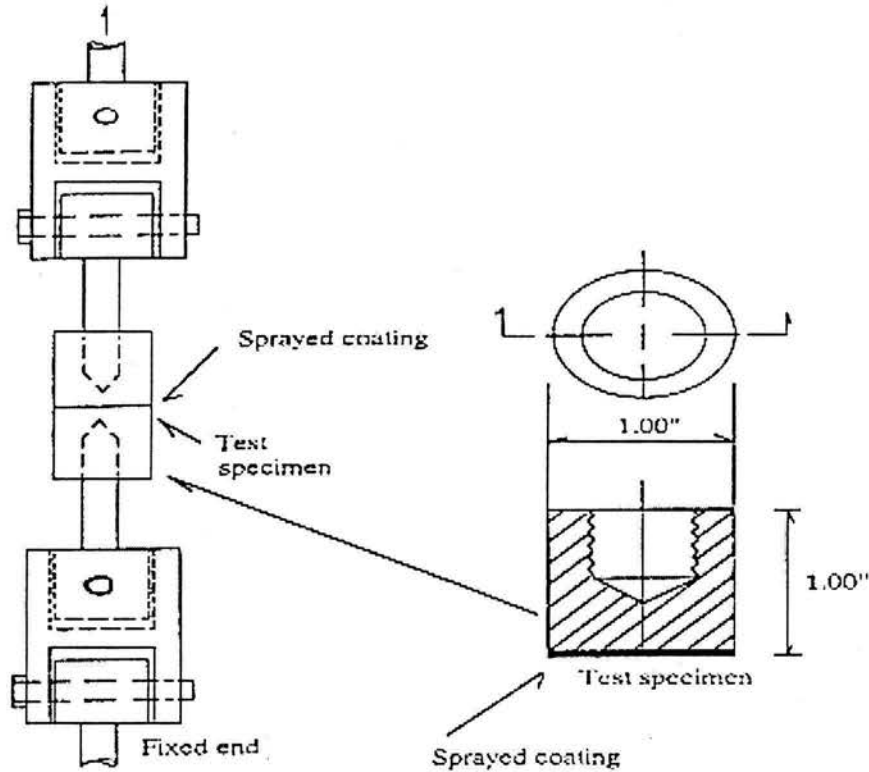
Probetas de adhesión de acuerdo a el diseño ASTM C 633[55].
